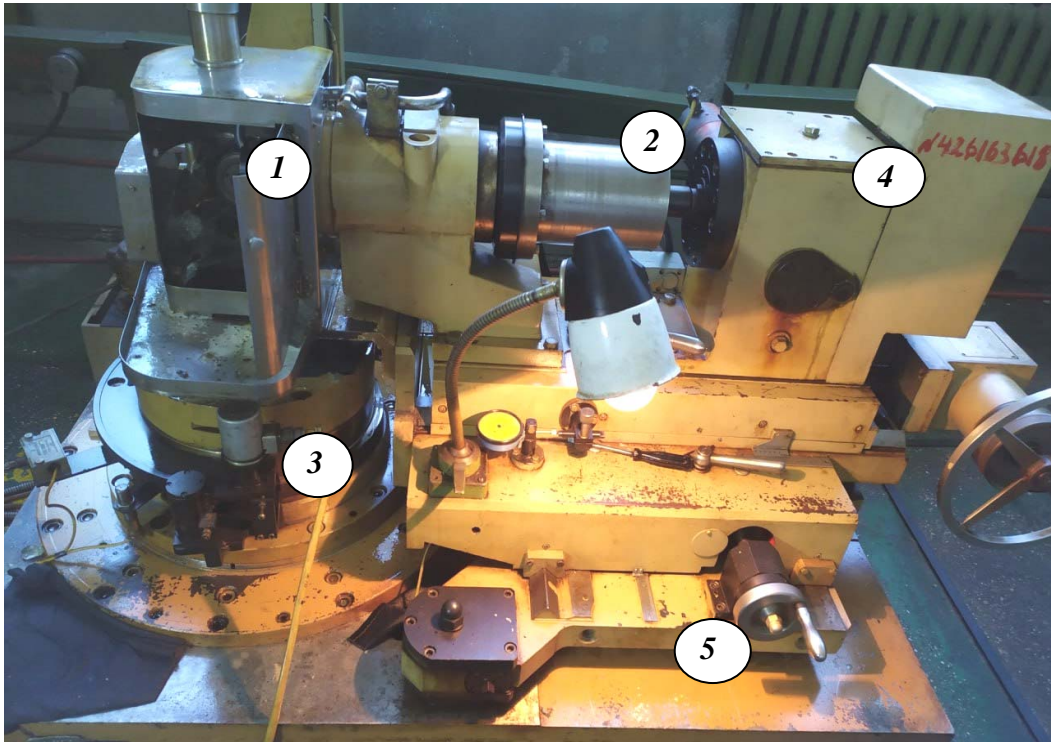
Общий вид сфершлифовального станка «Асфероид-100» модели Ф254-02:
